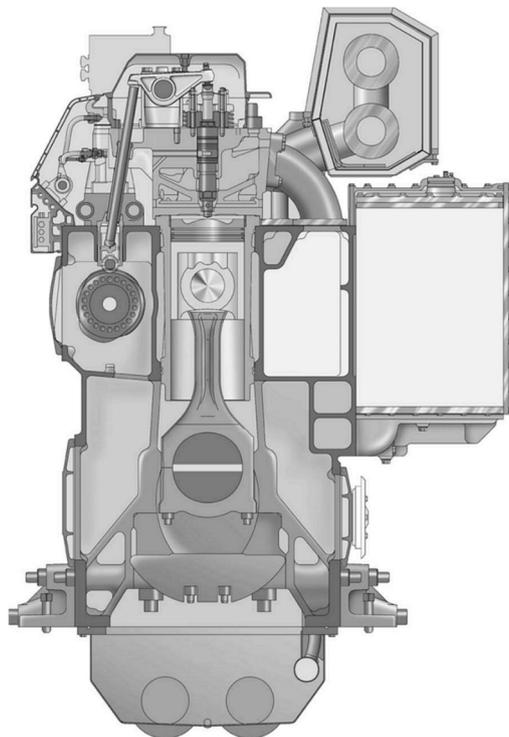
Corte lateral motor Wärtsilä 8L26. Fuente: [6].
